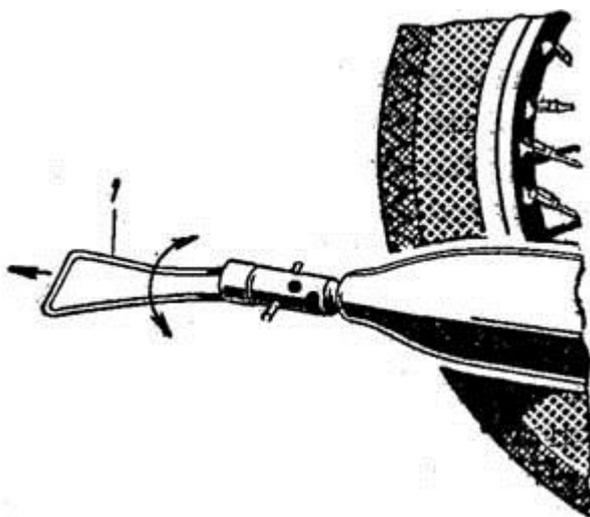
Извлечение трубки акустического фильтра из корпуса глушителя шума выпуска
